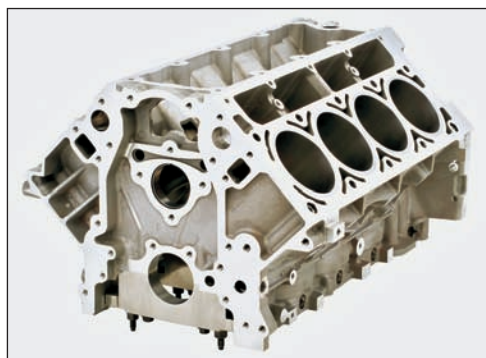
Алюминиевый блок цилиндров двигателя V8 с запрессованными «сухими» гильзами. В нижней части блока видна рама лестничного типа, с помощью которой крепится коленчатый вал
